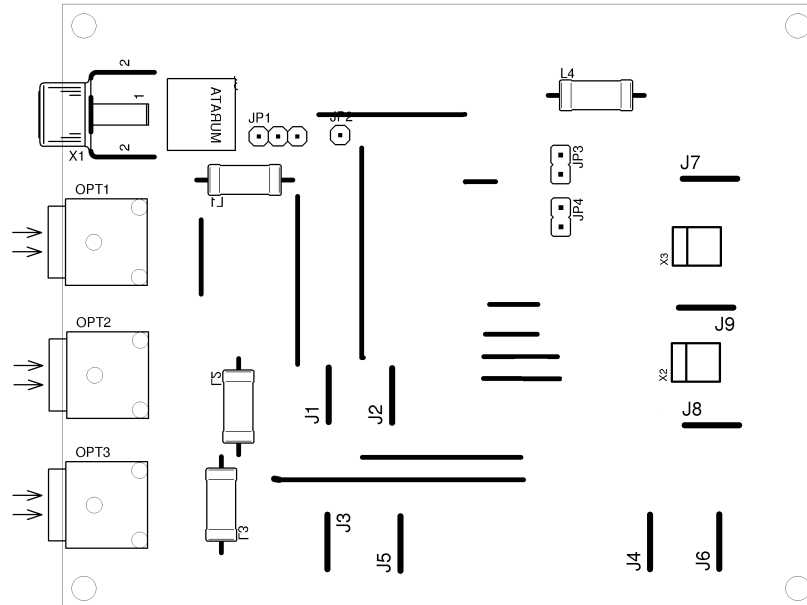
DPS D/A převodníku, strana bottom, 100 x 80 [mm], M1:1
